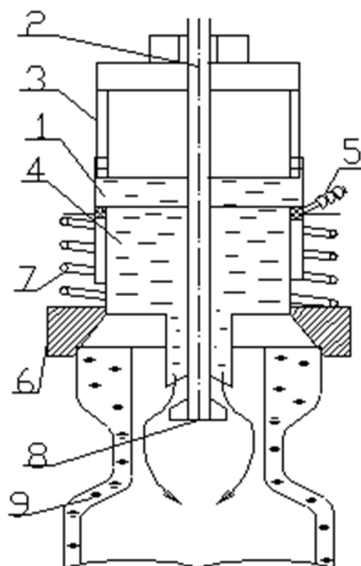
Схема об'ємного барометричного дозатора: 1 – мірний стакан; 2 – повітряна трубка; 3 – поршень; 4 – зливний патрубок; 5 – вхідний клапан; 6 – дзвіночок; 7 – пружина; 8 – зливний клапан; 9 – тара.
